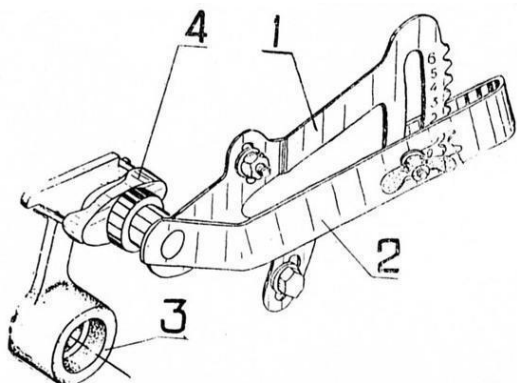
Установка отражательной вилки: 1 – сектор; 2 – рычаг вилки; 3 – шаблон; 4 – вилка
